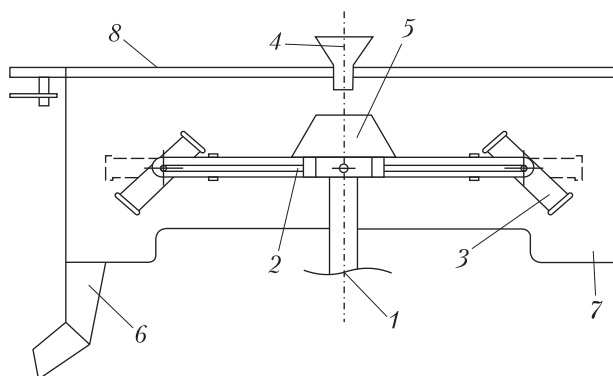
Стаканчиковая центрифуга: 1 – вал ротора; 2 – крестовина; 3 – фильтрующие стаканы; 4 – верхняя воронка; 5 – питающий патрубок; 6 – сливной патрубок; 7 – корпус центрифуги; 8 – крышка центрифуги
